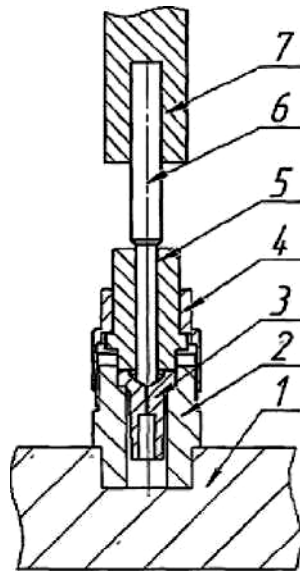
Оснащення для відновлення запірних клапанів ЕГФ типу CR фірми BOSCH: 1 - упорна плита; 2 корпус; 3 сідло клапана ЕГФ; 4 - гайка; 5 - направляюча проставка; 6 - притир; 7 - затискний патрон.
